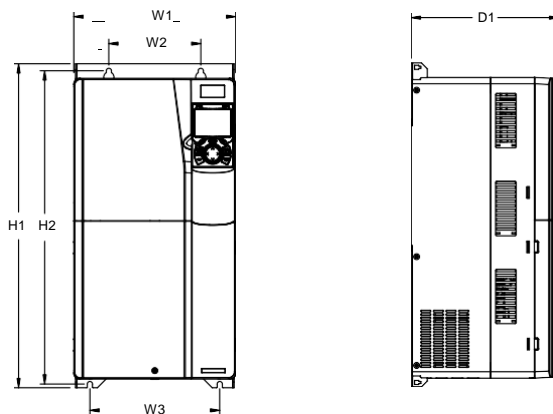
Схема настенного монтажа ПЧ напряжением 380 В, от 45 до 75 кВт.
